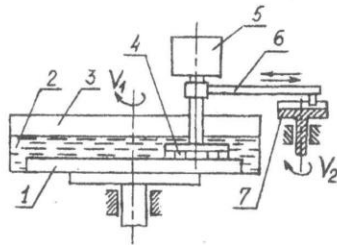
Схема установки для химико-механического шлифования твердосплавных пластинок под пайку:
